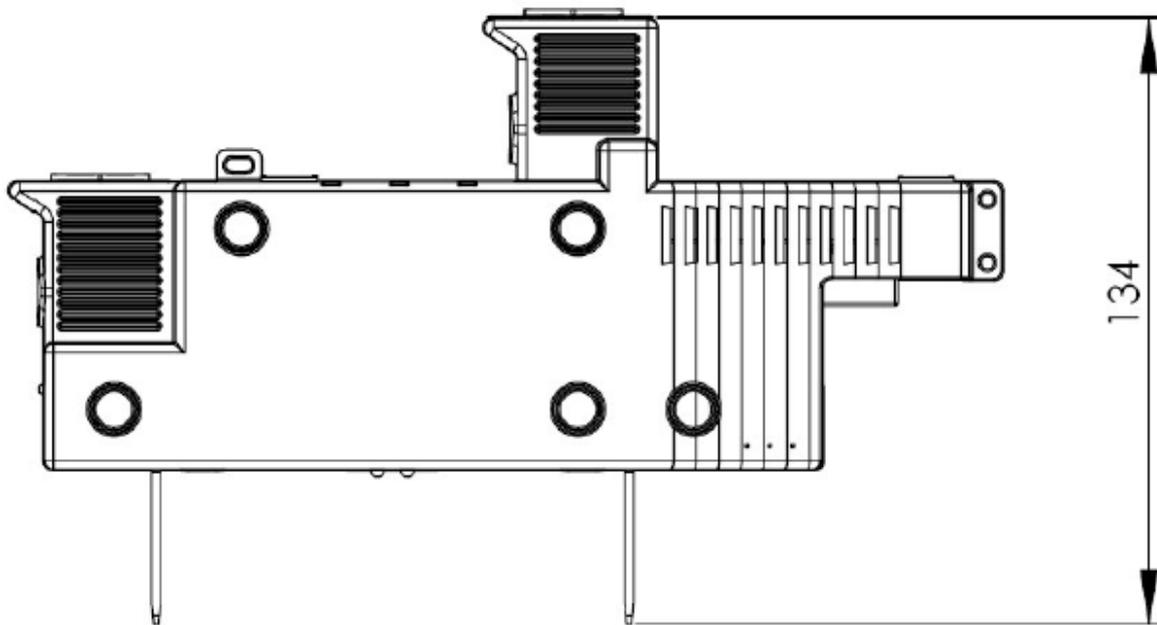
Dimensões do Módulo de Medição – Vista lateral
